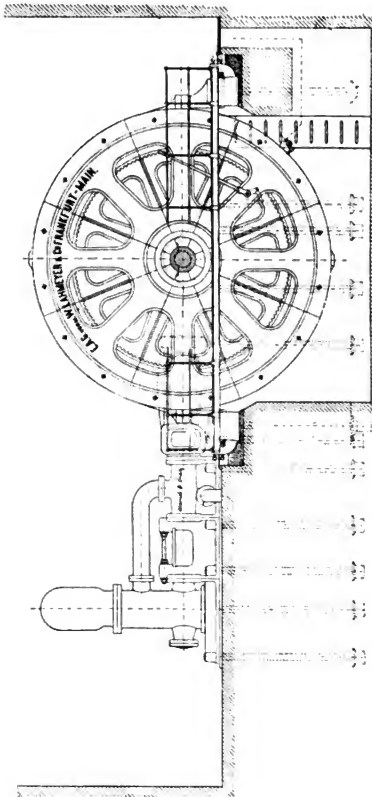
Wasserhaltungspumpe. Grundriss.
